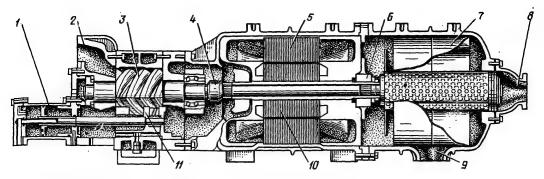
Винтовой бессальниковый холодильный компрессор фирмы «Duncham---Buch» (США):
